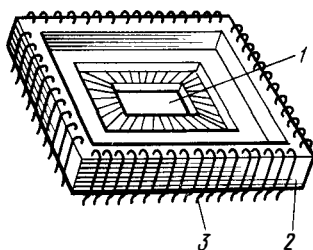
Пластмассовый кристаллодержатель с запрессованными гибкими вы-
